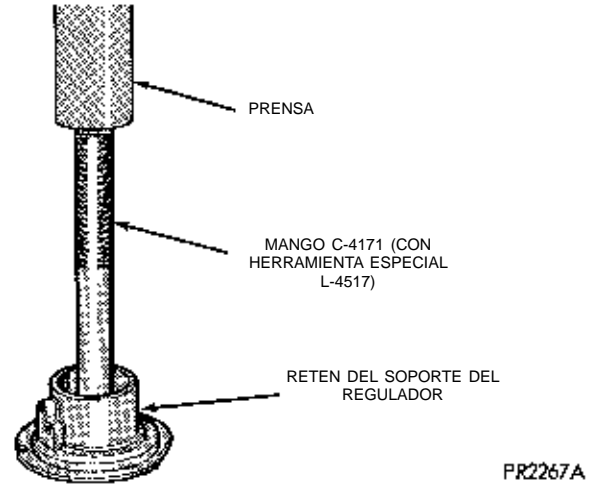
Desmontaje de la cubeta de cojinete del retén del soporte del regulador
